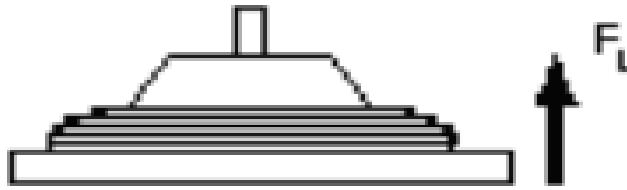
Fuerza de desplazamiento en ventosa de succión caso 1
